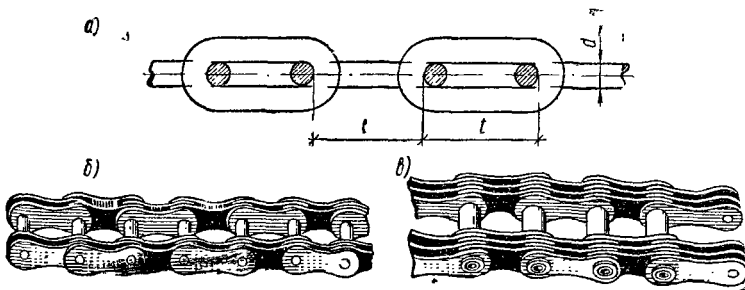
Сварные *а* и пластинчатые *б, в* цепи
